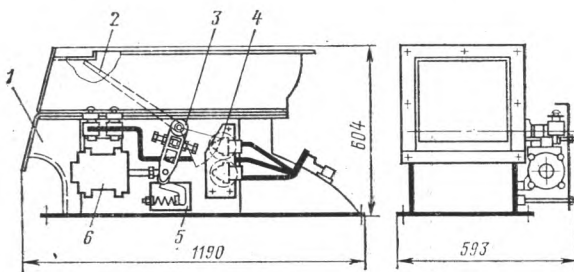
Устройство переключения воздуха типа УПВ-5: 1 — патрубок; 2 — заслонка; 3 — рычаг; 4 — электрический фиксатор; 5 — пружинный фиксатор; 6 — пневматический привод
